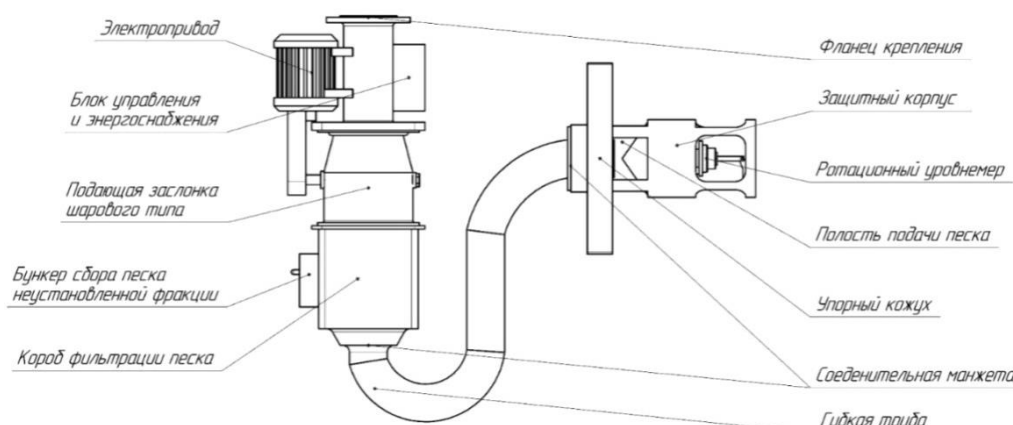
Устройство автоматизированного рукава для заправки локомотива песком
